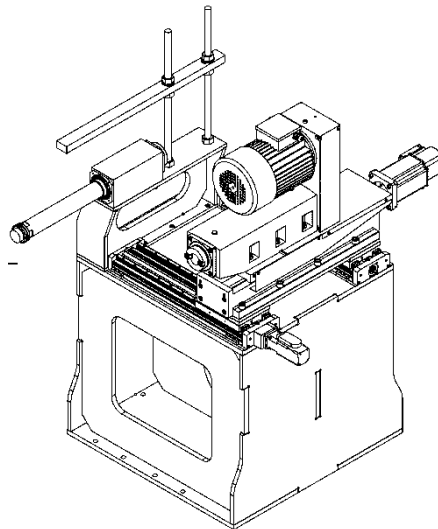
Perspetiva isométrica “Assembly final CM”.
